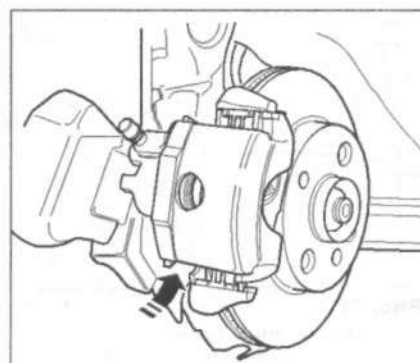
Установите тормозной суппорт (стрелка) и затяните болты его крепления.
